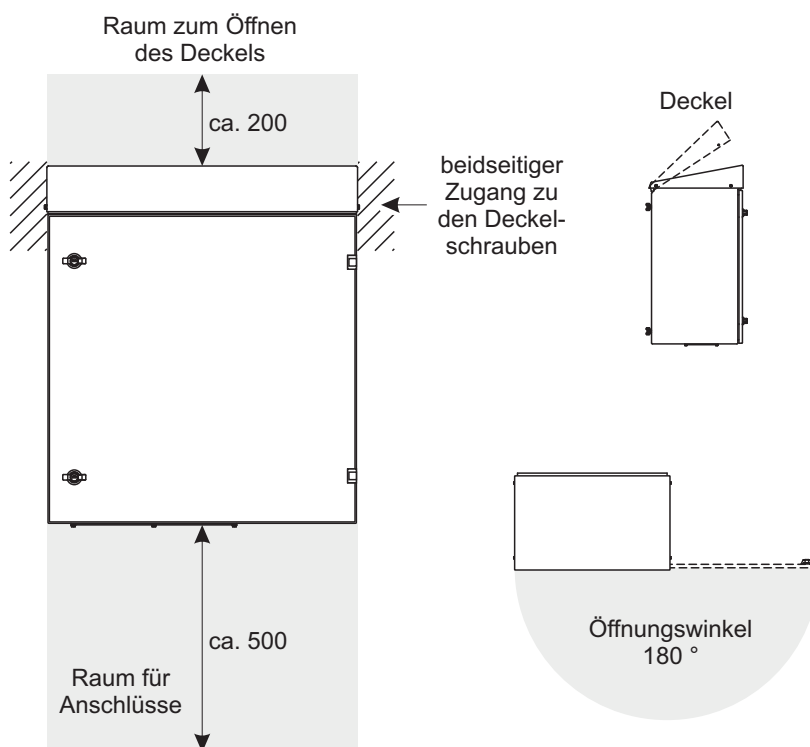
Maßzeichnung P 700 IQ Gehäuse (Maße in mm)
